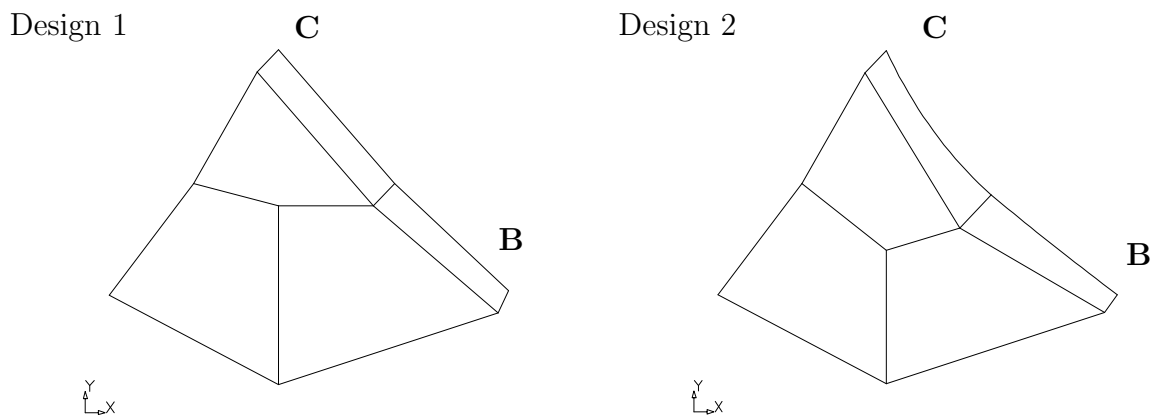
Ausbildung der Schweißnaht für das Design 1 und 2
